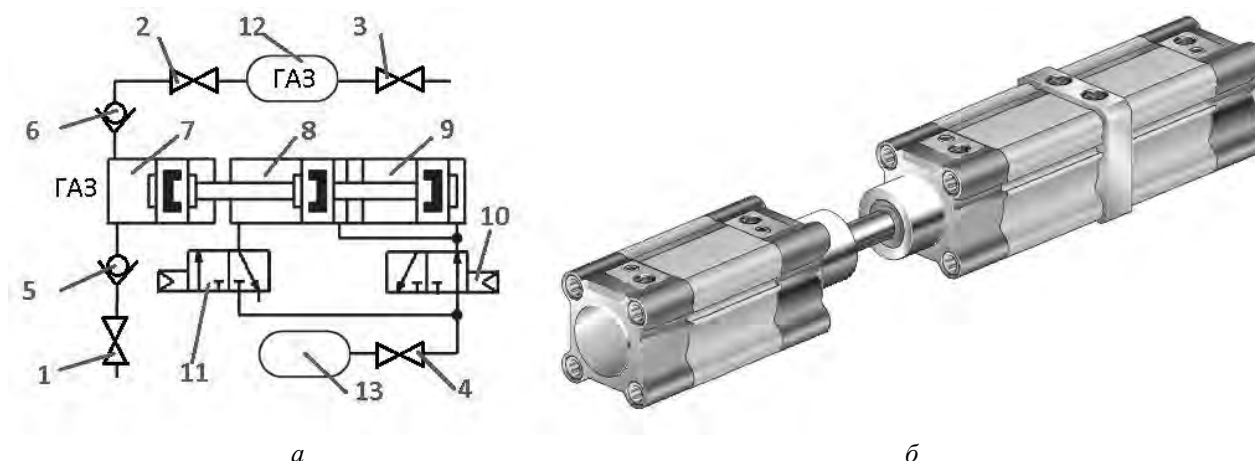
Пневматична схема відбирання природного газу (а) та зовнішній вигляд циліндра-дозатора із пневматичним приводом (б)
